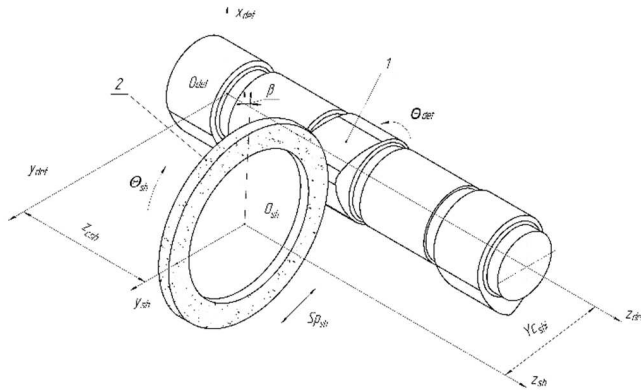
Схема обробки розподільчого вала фірмою Junker
